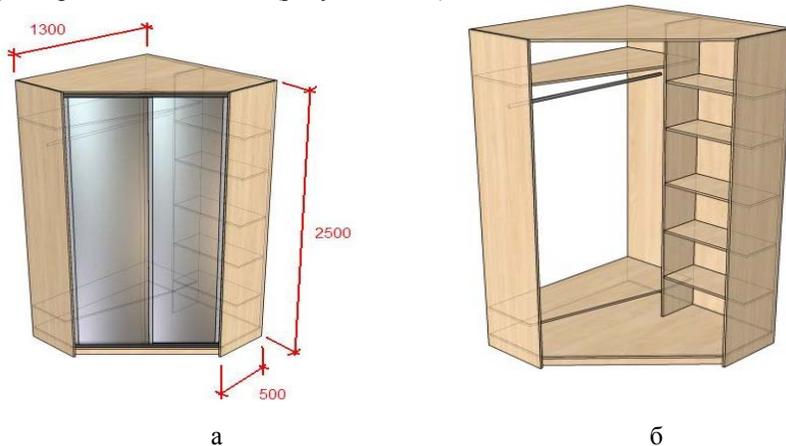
Шкаф угловой гардеробный: а – внешний вид; б – внутренняя конструкция
